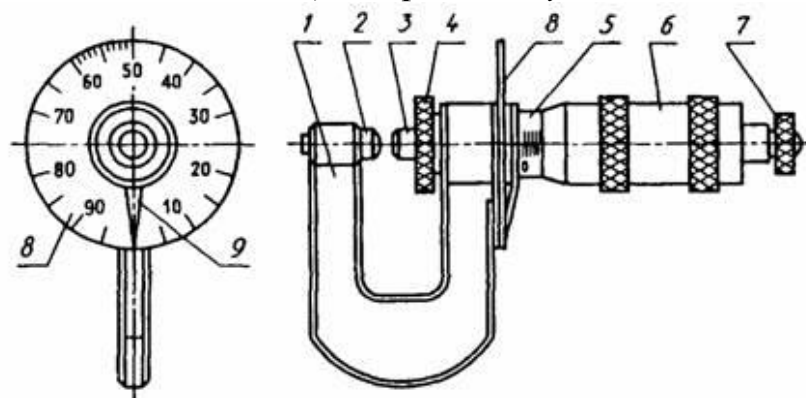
Тип МЛ. Мікрометр листовий: 1 - скоба; 2 - п'ята; 3 - мікрометричний гвинт; 4 - стопор; 5 - стебло; 6 - барабан; 7 - тріскачка (фрикційна); 8 - циферблат; 9 - стрілка
